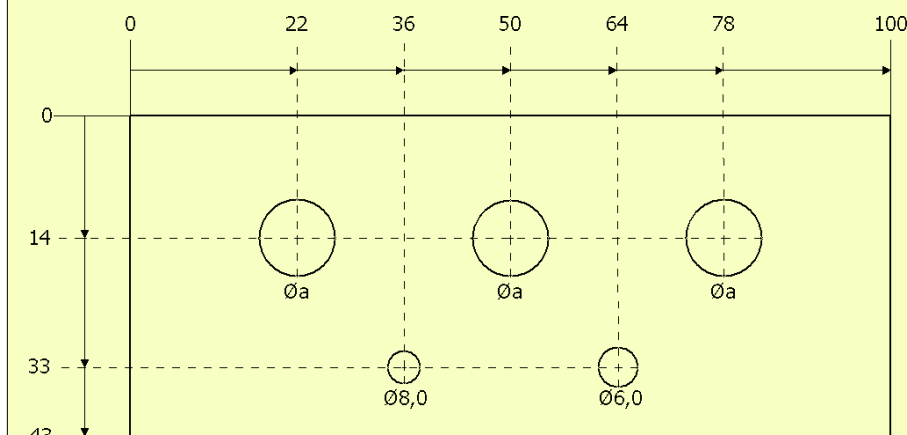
Maßskizze der Rückwand für das realisierte Gehäuse
